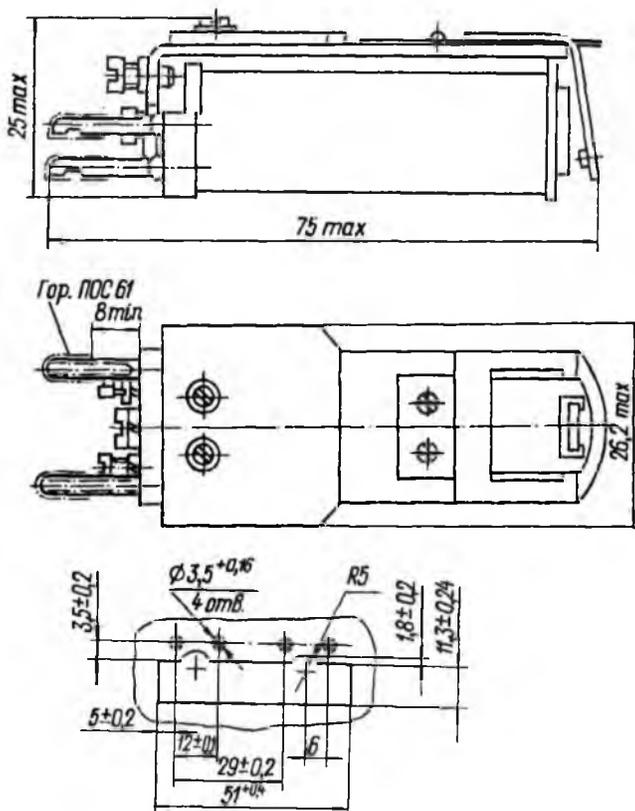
Конструктивные данные и разметка для крепления дросселя РКМ1
